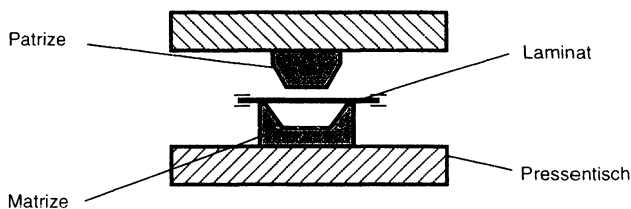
Umformen mit Metallwerkzeugen (Matched Metal Molding)
